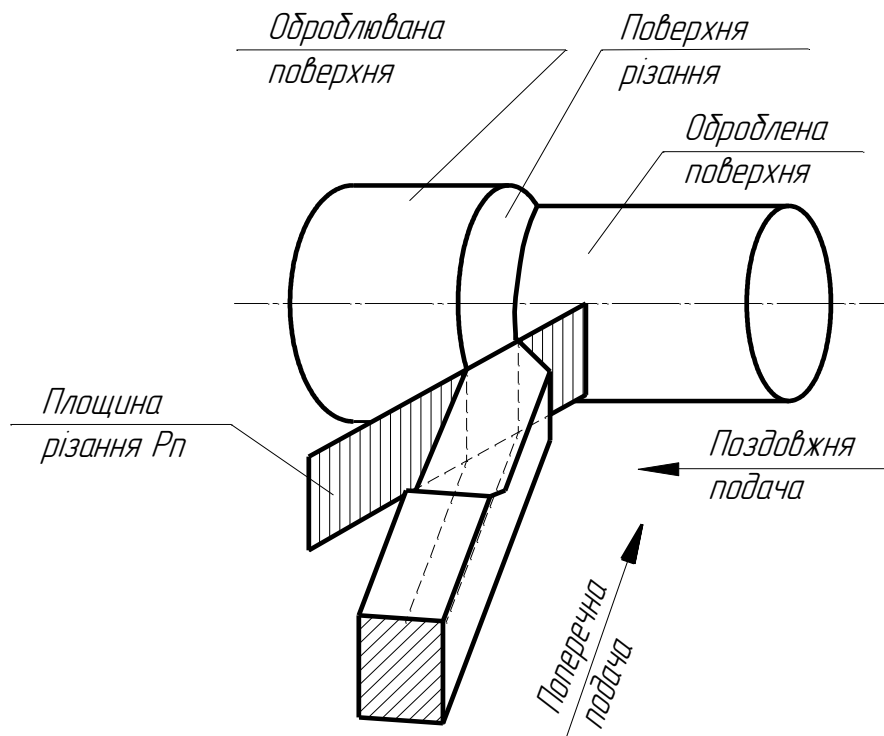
Види поверхонь на оброблюваній заготовці
